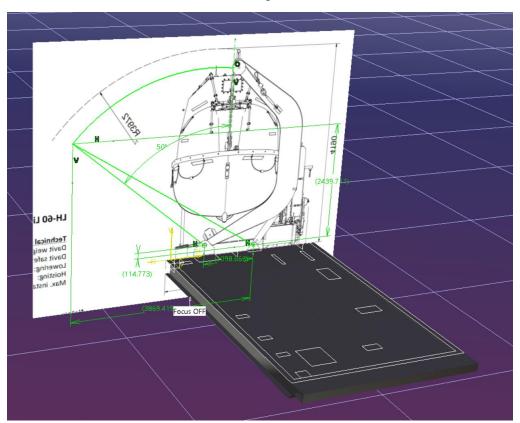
Proyección de plano del pescante en Catia v5. 2025. Plano propiedad de Viking. Modelo LH-60. Fuente: 3D Elaboración propia, Plano: https://www.viking-life.com
